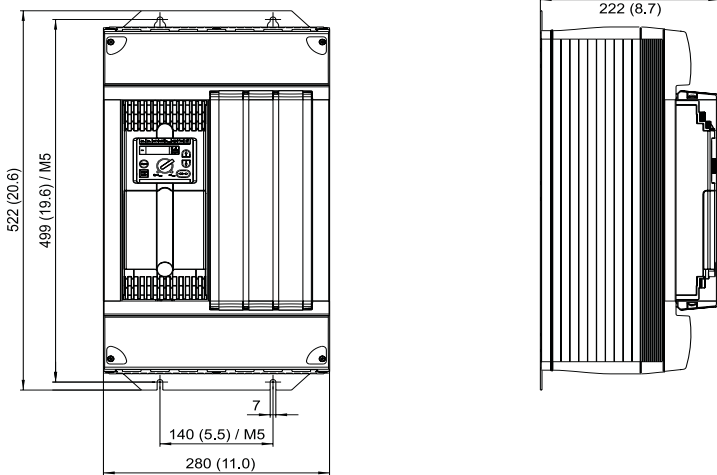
MOVITRAC® 07 / типоразмер 4 / 3-фазный на 230 В_~
